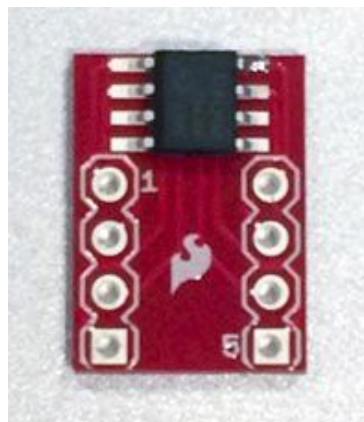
Установка микросхемы в корпусе SOIC-8 на плату BOB.
